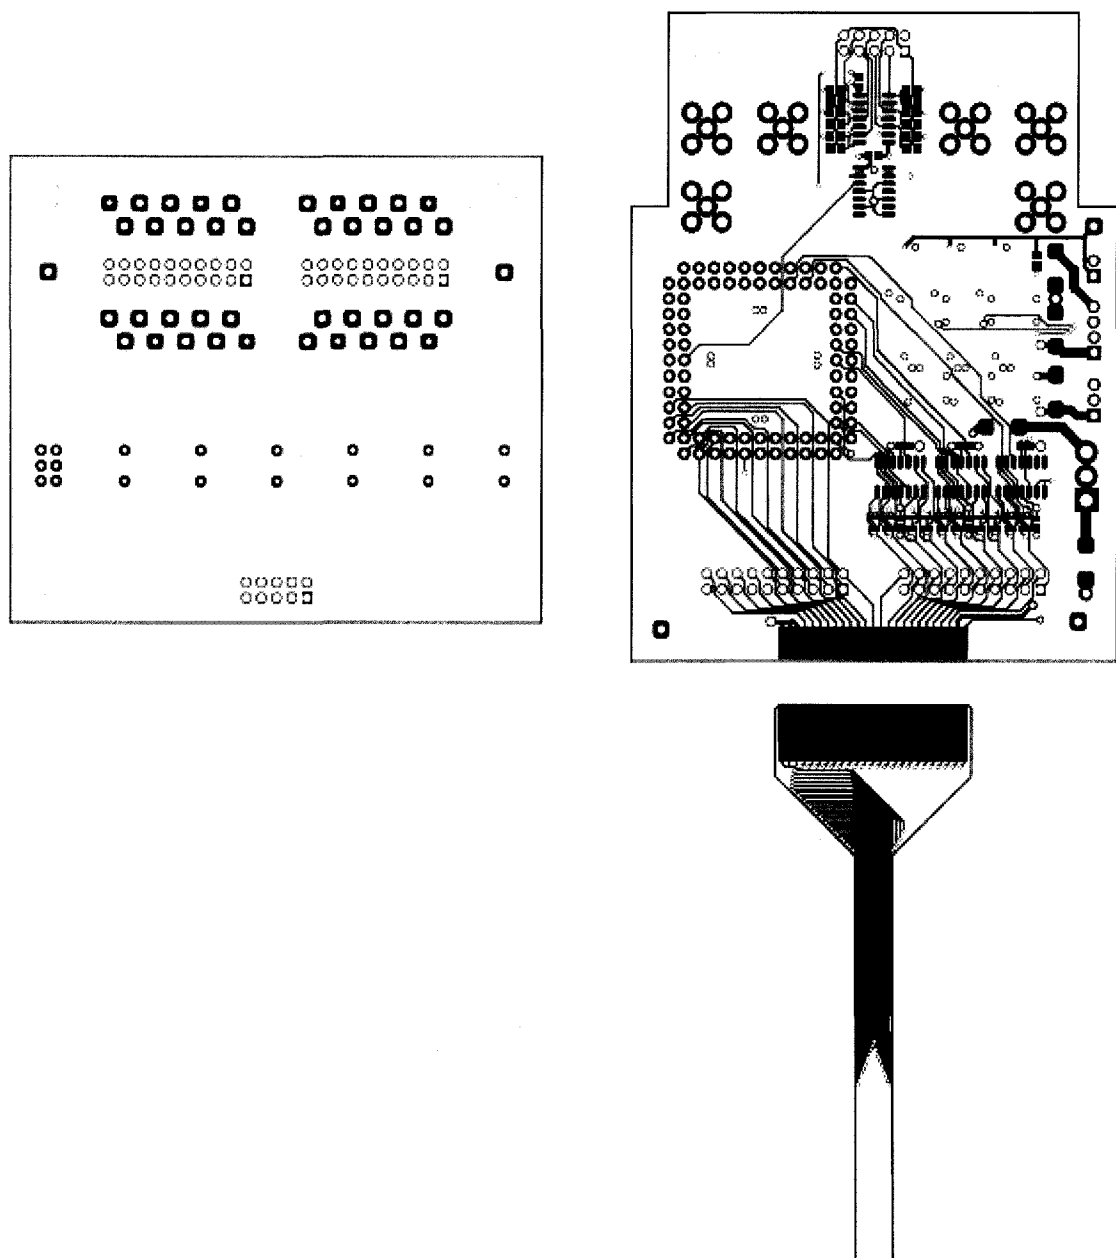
Le dessin de masque du circuit imprimé (vue recto)
